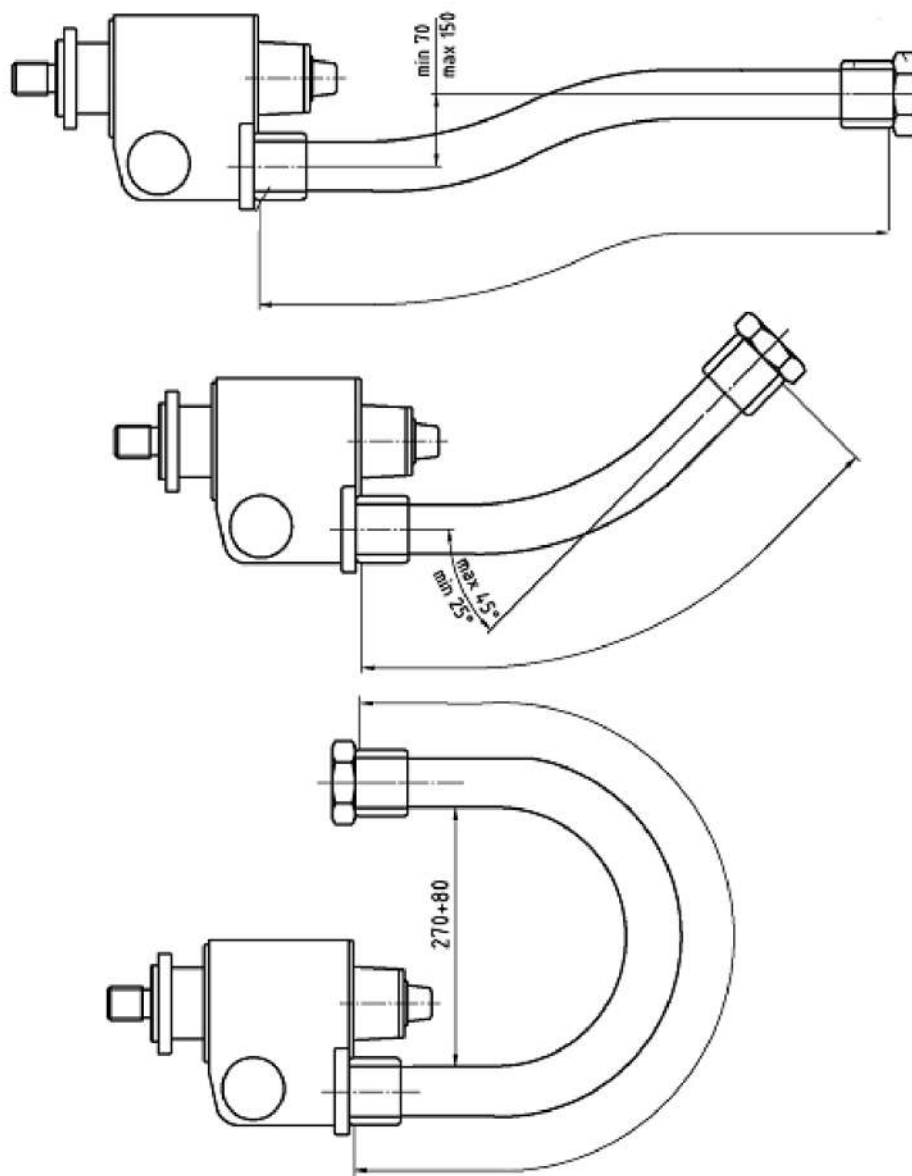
Примеры установки для напорной стороны, с длиной шланга для различных угловых соединения для шлангов
